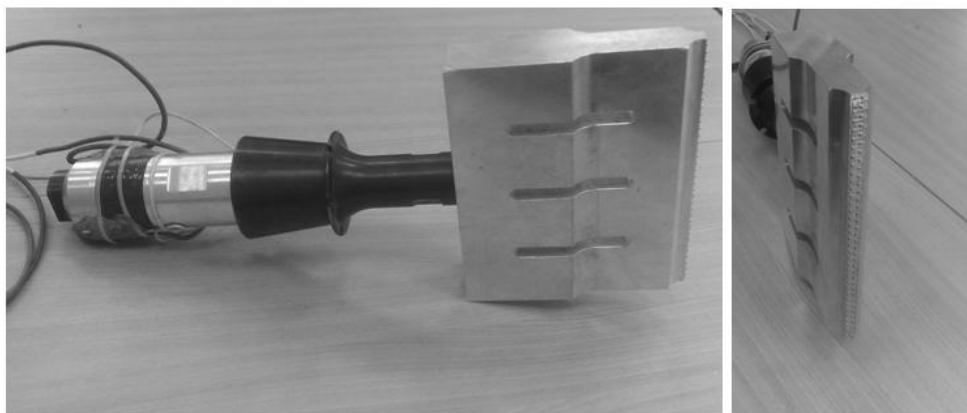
Волновод инструмент для сварки полимерных лент
